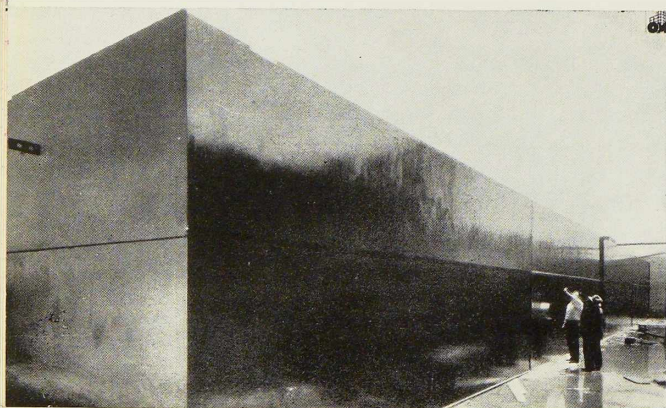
Vue de deux des trois réservoirs à essence construits par soudure électrique au moyen d'électrodes enrobées.
